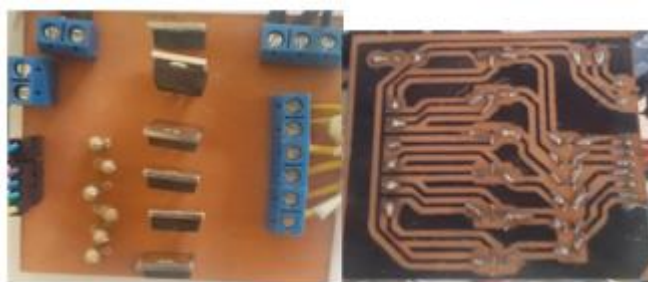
Placa de las barras led vista frontal y pistas soldadas vista posterior
